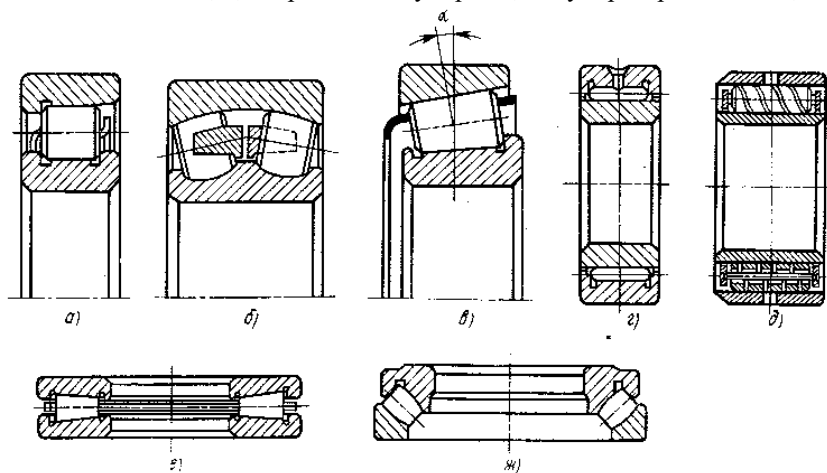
Основные типы роликоподшипников: а – радиальные с короткими (или с длинными) цилиндрическими роликами; б – радиальные с бочкообразными роликами двухрядные
